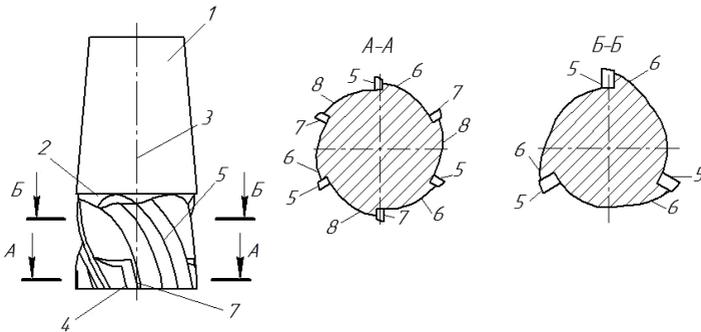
Эскиз концевой фрезы: 1 – хвостовик, 2 – тело, 3 – ось, 4 – торцевая плоскость, 5 – основные винтовые режущие зубья, 6 – затылки основных режущих зубьев, 7 – дополнительные режущие зубья, 8 – затылки дополнительных режущих зубьев
